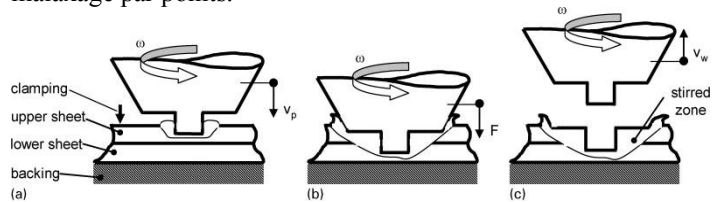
Principe du soudage par point par friction malaxage [1]
